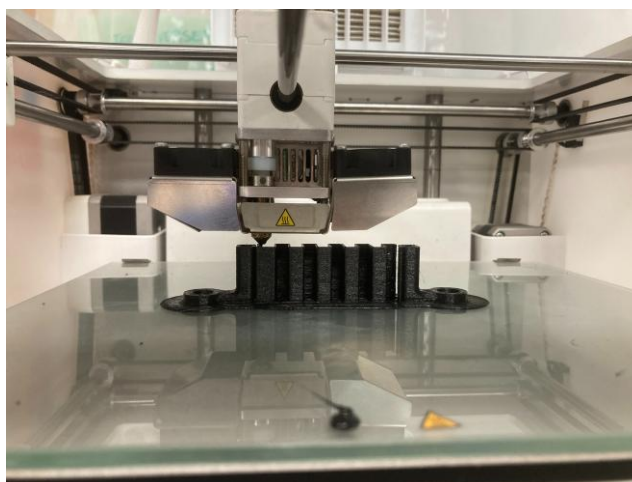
Impression 3D de la poignée du couvercle en cours de fabrication
